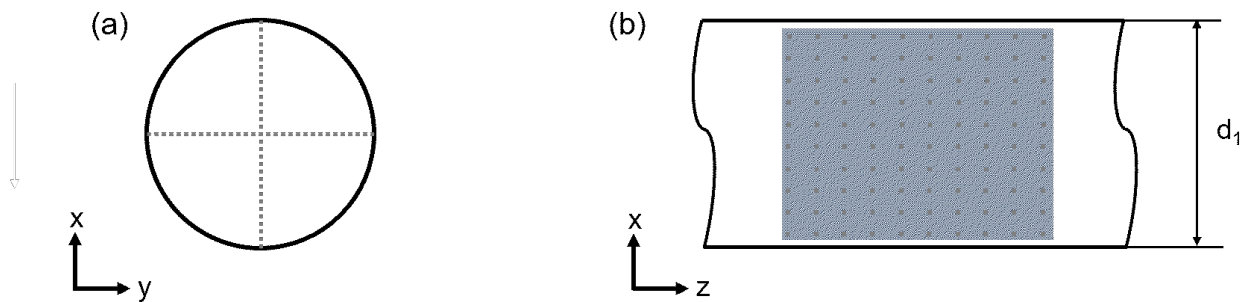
Punkte der Härtemessungen: a) Querschnitt; b) Längsschnitt.
